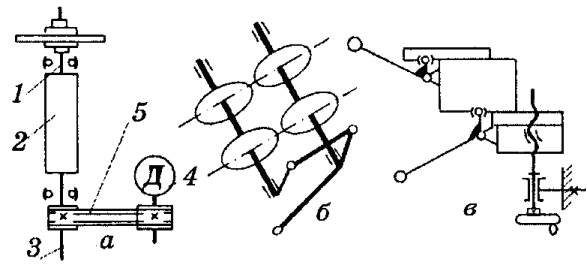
Кінематична схема механізмів комбінованого верстата: а – механізм різання; б – механізм регулювання положення переднього стола фугувального агрегату; в – механізм переміщення стола свердильно-пазувального агрегату; 1 – пиловий агрегат; 2 – поздовжньо-фрезувальний; 3 – свердильний; 4 – електродвигун; 5 – клинопасова передача
